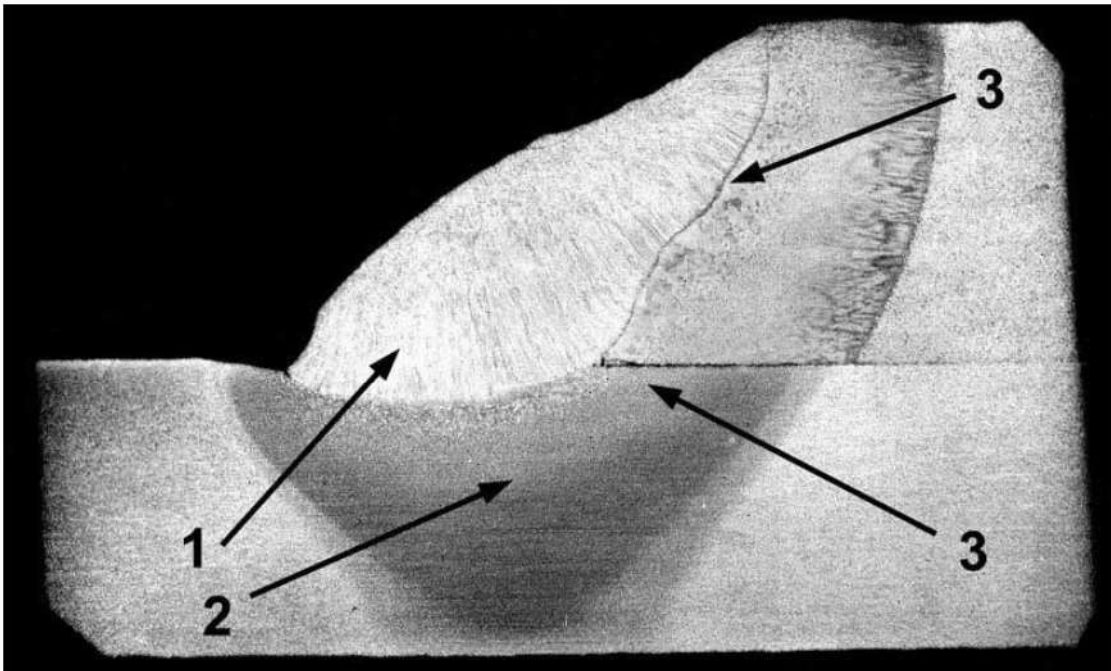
Aspecto de la sección transversal (figura 3). El tubo y la parte del refuerzo (soldadura, flecha 1) presentan alteraciones microestructurales (flecha 2) por el proceso de soldadura. Existen fallas en el encuentro entre la soldadura, el tubo y el refuerzo (flecha 3). Reactivo de yodo.
